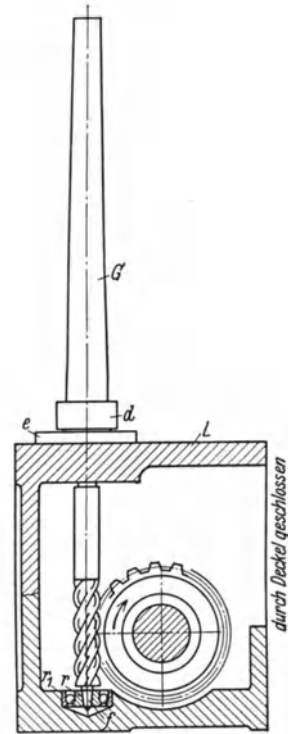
Schraubenradantrieb für die Perfektspindel.
